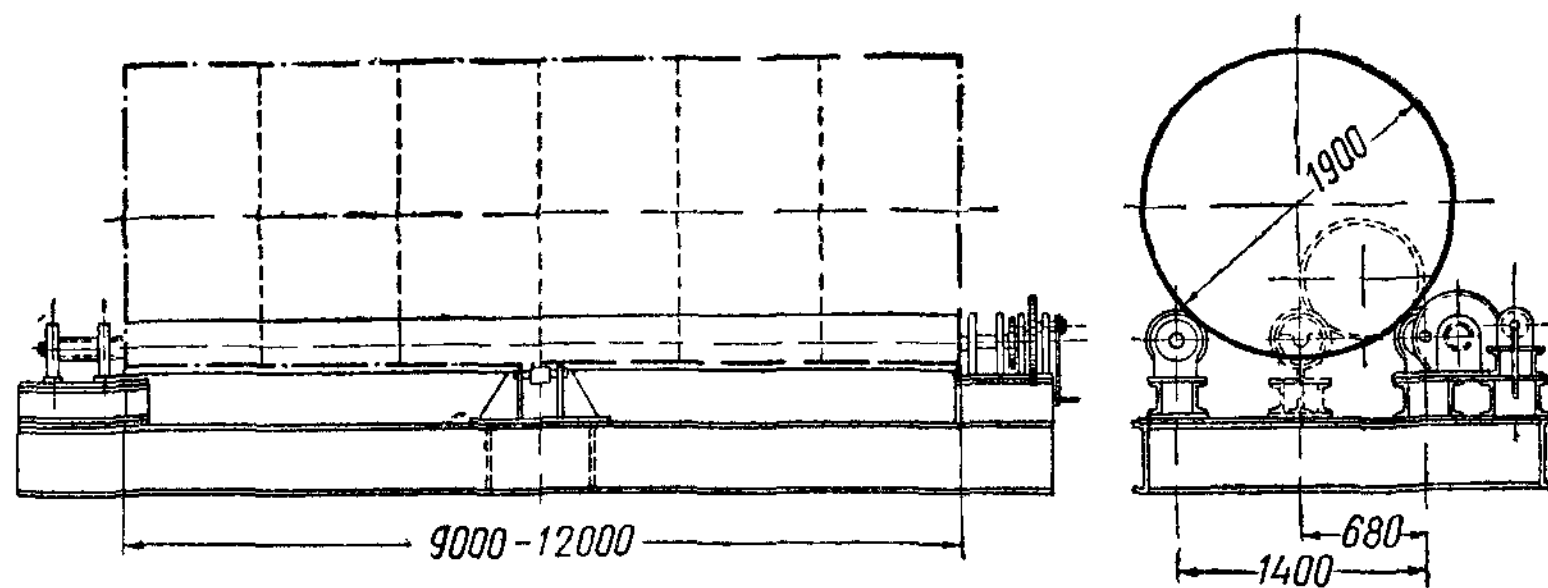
Трубчатый стенд для сборки габаритных цилиндрических конструкций
